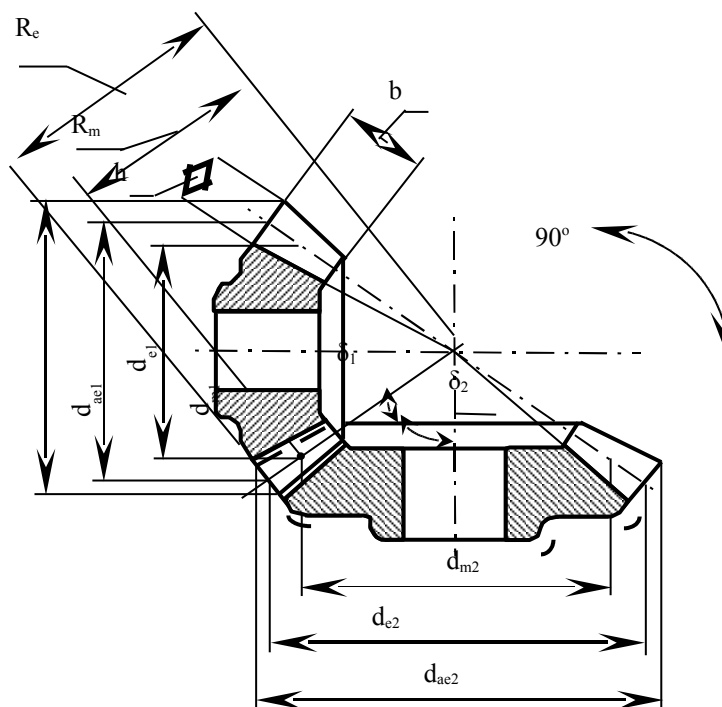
Основные геометрические размеры конической зубчатой передачи
